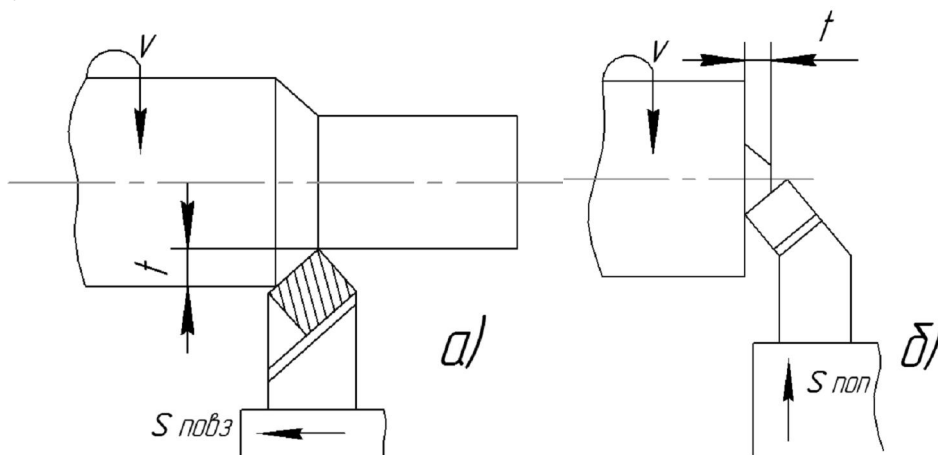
Схеми робочих рухів при токарній обробці:
